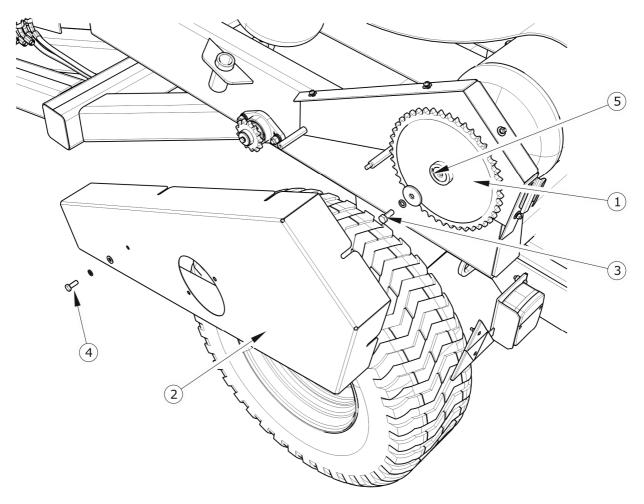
Desmontaje de la rueda motriz del rodillo
